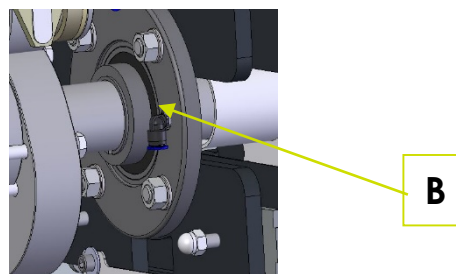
Montage du système d'entraînement Conduites de graissage sur le côté droit
